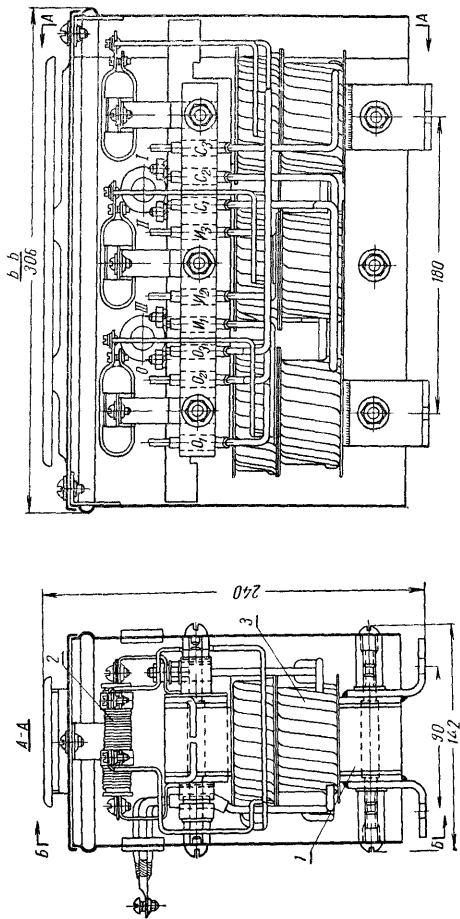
Общий вид регулятора напряжения генератора типа СГТ:
